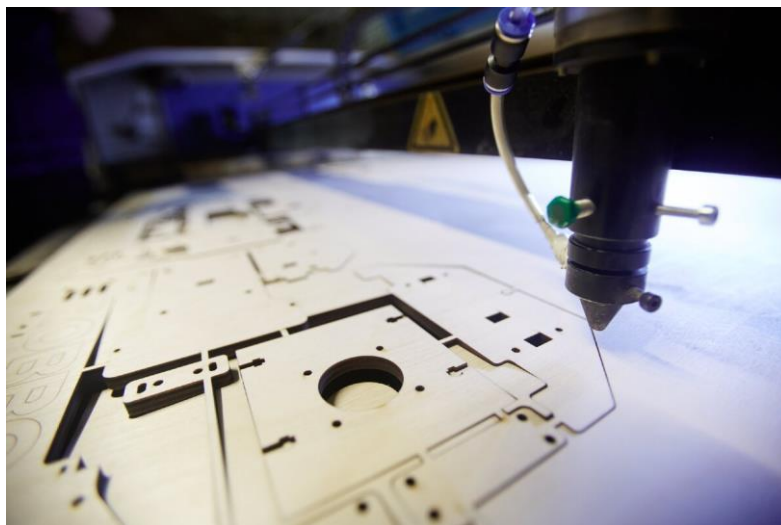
процес виготовлення деталей на лазерному верстаті
